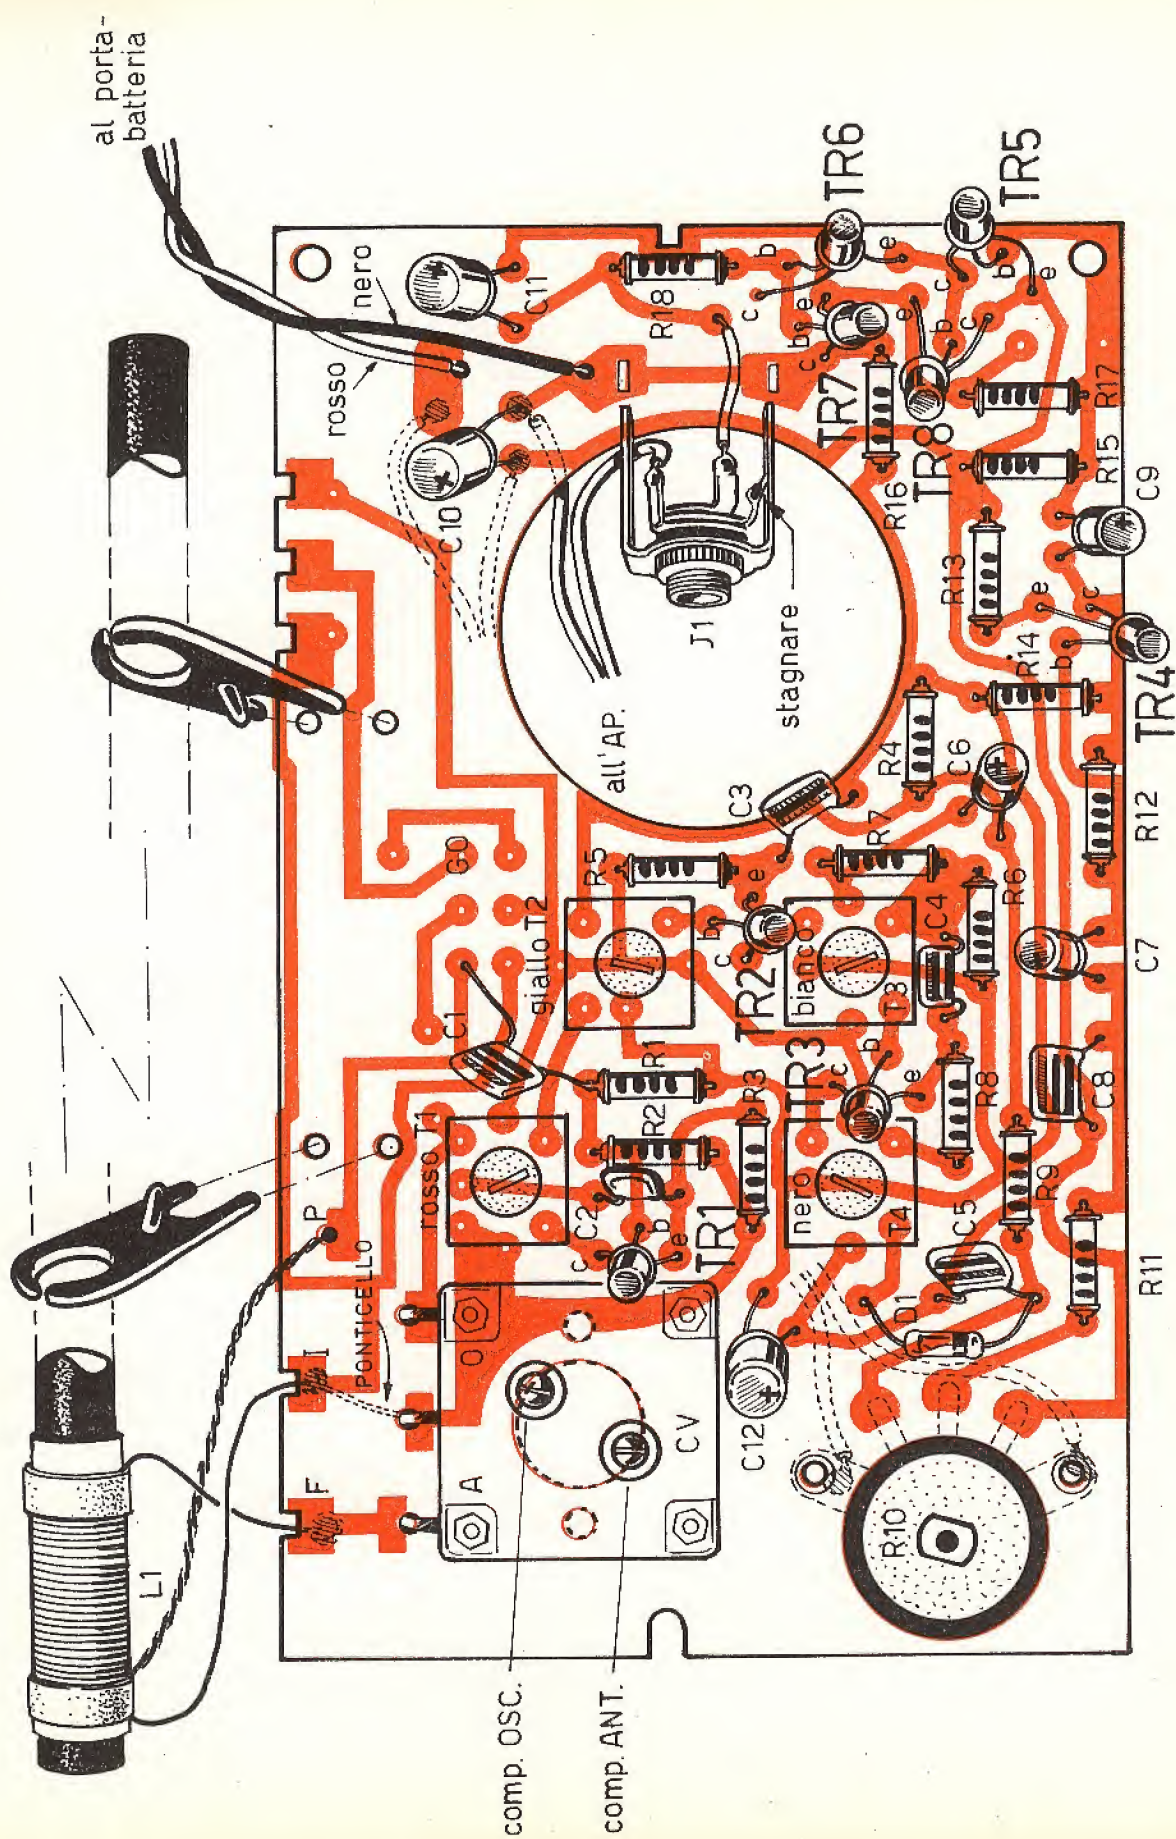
Questo disegno, nel quale è indicata la posizione esatta di fissaggio di ciascun componente, deve essere attentamente seguito durante tutto il lavoro di montaggio del TICO-TICO. Si tenga presente che il circuito stampato è da considerarsi "visto" in trasparenza, dato che ogni elemento viene applicato sulla faccia, della basetta rettangolare, opposta a quella in cui sono presenti le piste di rame, nelle quali si effettuano le saldature a stagno dei terminali di tutti i componenti elettronici. Il lavoro di montaggio del ricevitore comincia con l'applicazione sulla basetta della presa per auricolare (J1). Questo elemento richiede la particolare saldatura a stagno chiaramente indicata nel disegno. Poi si applicano, nell'ordine, il potenziometro R10, le resistenze, i transistor, i condensatori, il condensatore variabile CV, l'oscillatore, i trasformatori di media frequenza, la bobina L1, l'altoparlante e le pile.
